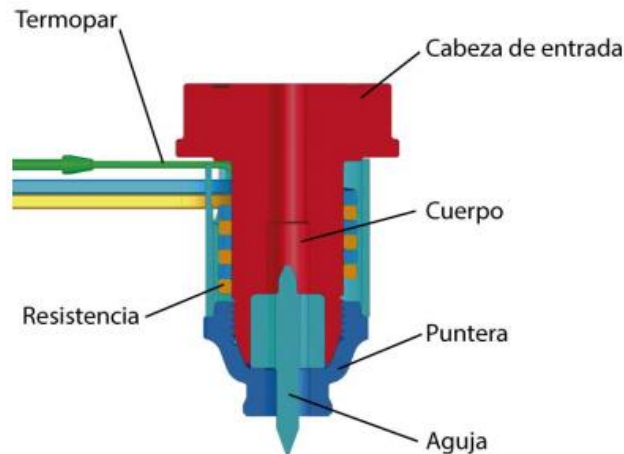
Componentes de una boquilla. Fuente: F. Del Moral.
